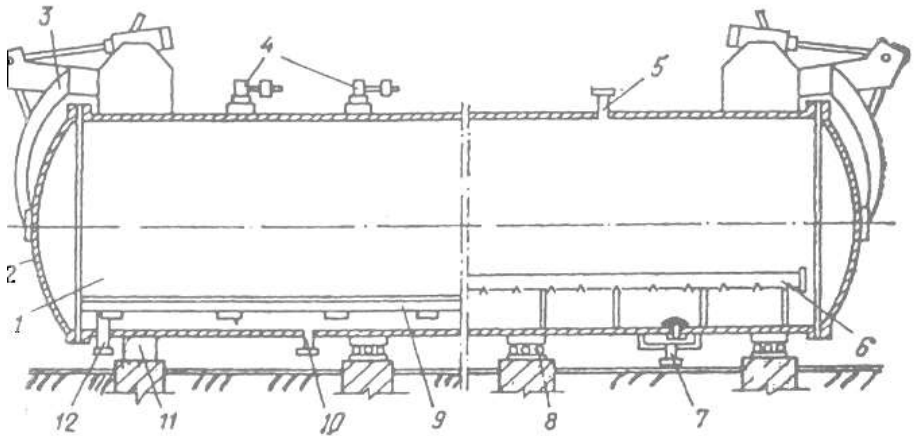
Схема автоклаву: 1 – корпус; 2 – кришка; 3 – механізм кришки; 4 – попереджувальний клапан; 5 – патрубок для перепуску пари; 6 – перфорована трубка; 7 – патрубок для виведення конденсату; 8 – рухливі опори; 9 – рейки; 10 – вакуум-система; 11 – нерухома опора; 12 – патрубок для введення пари
